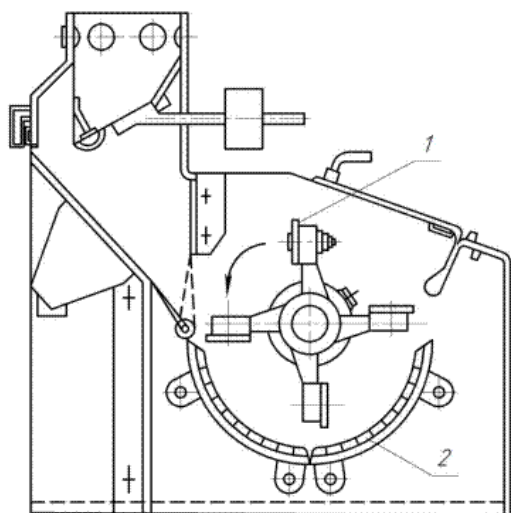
Схема машини зі сталевими билами і декою: 1 – било; 2 – дека
